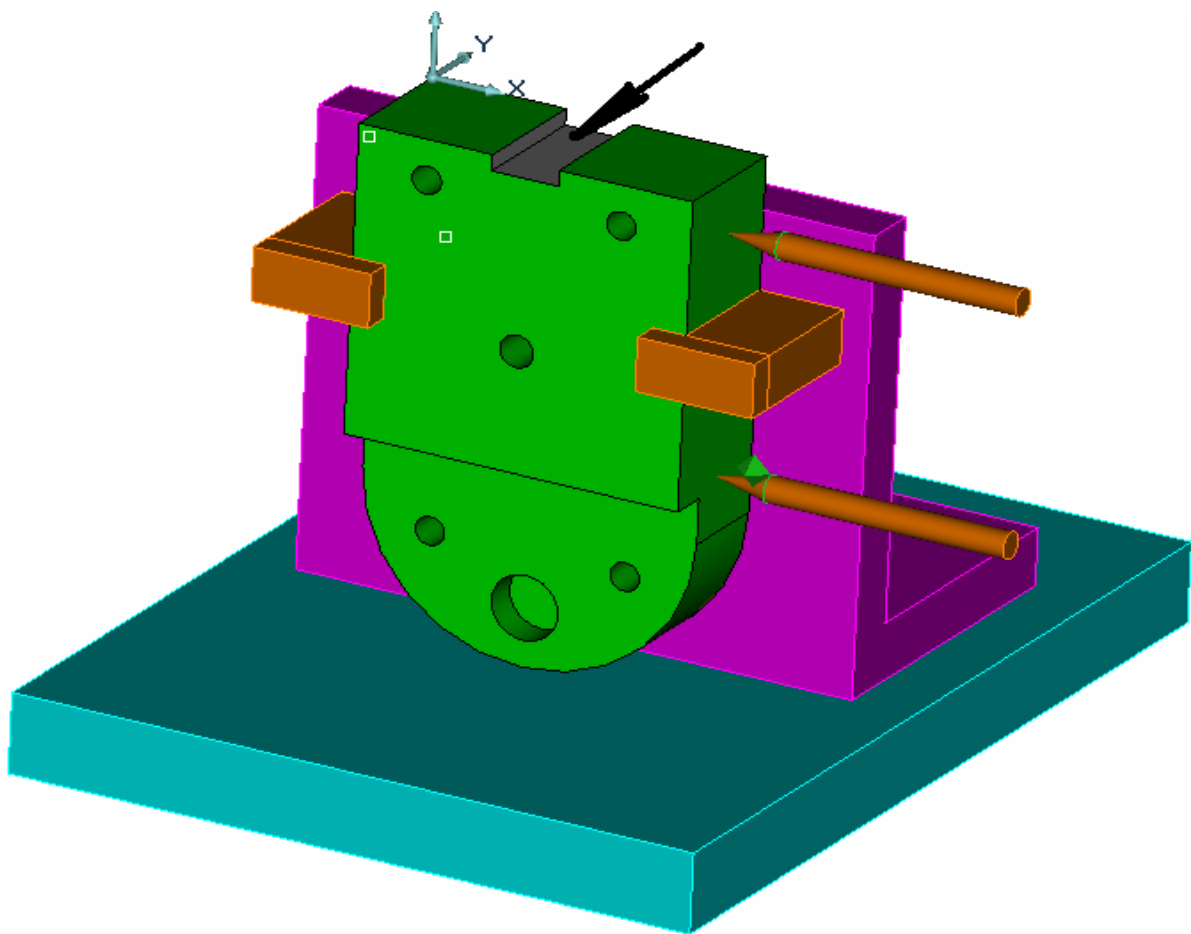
Переход на завершающей фрезерной операции 015: выполнение сквозного паза
